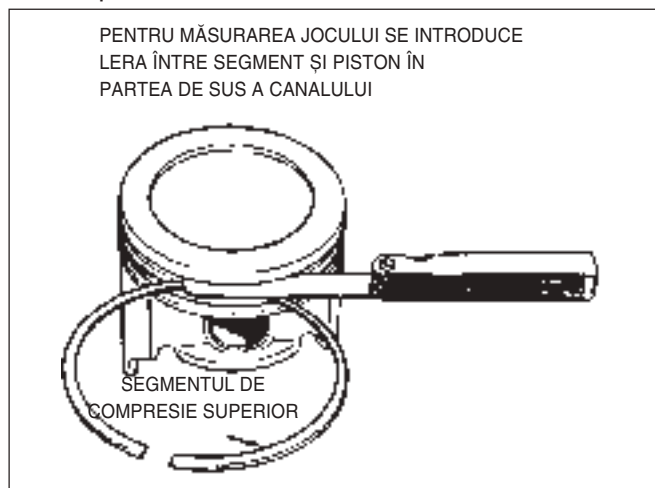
Măsurarea jocului segmentului în canalul de pe piston
